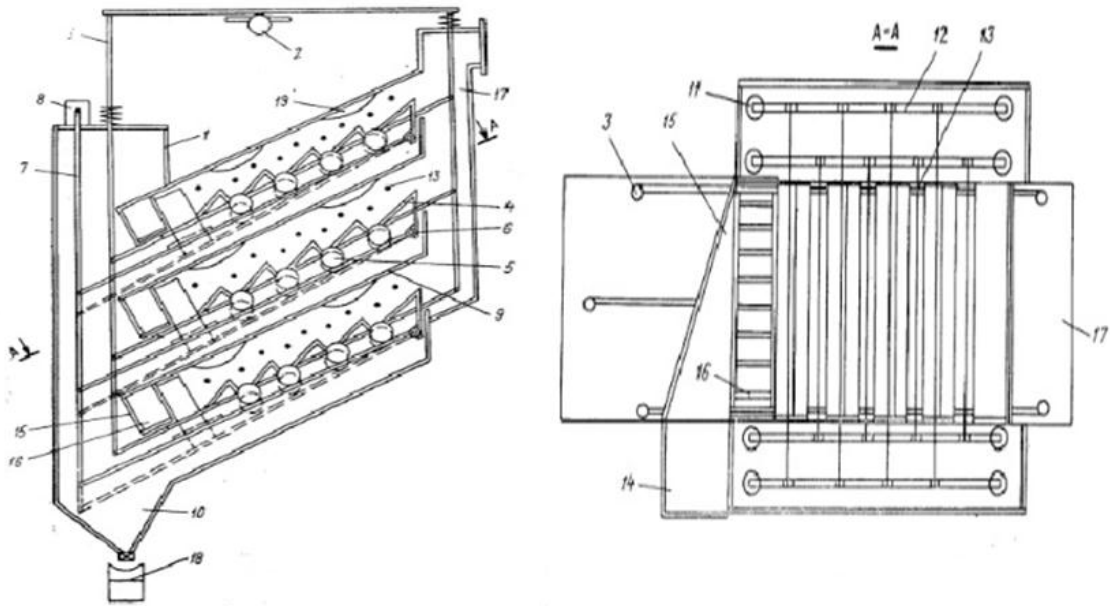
Сухой электрофильтр: а) общий вид; б) разрез по А-А; 1 – корпус; 2 – вибрационное устройство; 3 – штанги; 4 – верхняя решетка; 5 – нижняя решетка; 6 – шарниры; 7 – шток; 8 – наполнительный механизм; 9 – индивидуальный бункер; 10 – бункер-накопитель; 11 – изоляторные коробки; 12 – рамки; 13 – коронирующие электроды; 14 – общий подводящий газоход; 15 – насадки равномерной передачи; 16 – делительные перегородки; 17 – отводящий газоход; 18 – транспортер; 19 – плоскости поджатия
